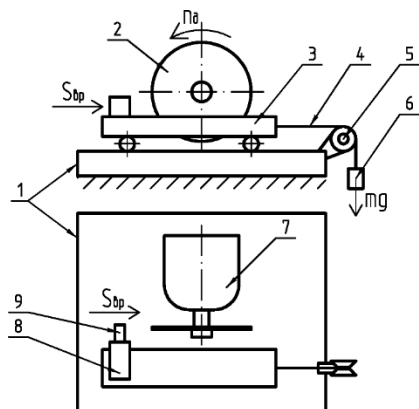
Технологическая схема установки для распиливания образцов испытываемым диском
